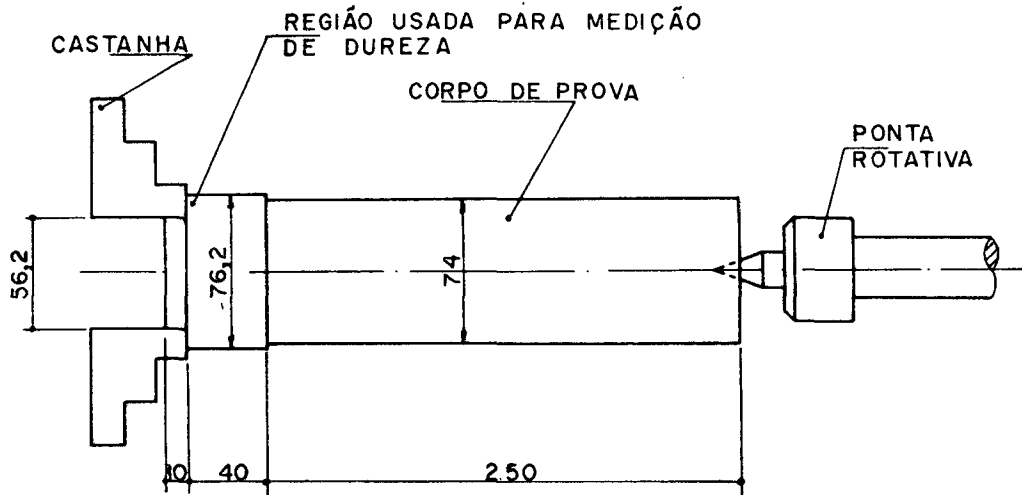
Dimensões e fixação dos corpos de prova para ensaio de usinabilidade.
